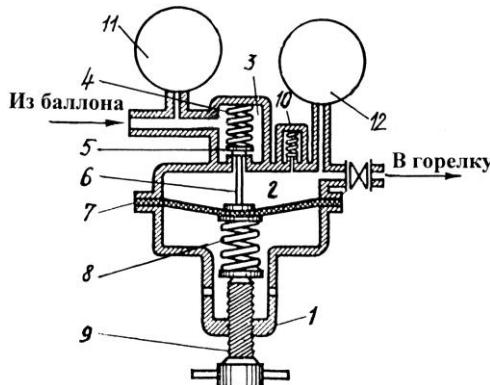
Схема однокамерного редуктора: 1 – корпус редуктора; 2 – камера низкого давления; 3 – камера высокого давления; 4 – запорная пружина; 5 – клапан высокого давления; 6 – толкател; 7 – мембрana; 8 – главная пружина; 9 – регулировочный винт; 10 – предохранительный клапан; 11 – манометр высокого давления; 12 – манометр низкого давления
